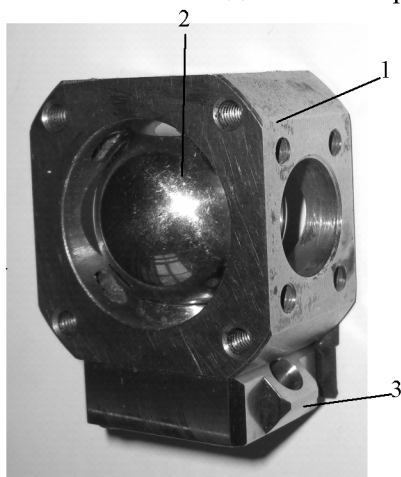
Установка вставки з нанесеним металполімером у корпусі шарніра
